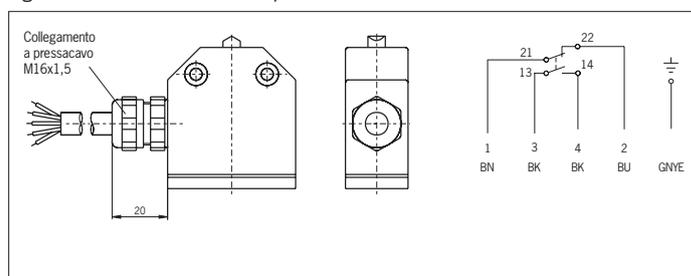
Dimensioni/schema di collegamento SN01.558X... con cavo di collegamento (cavo PUR, 5x0,5 mm²)
